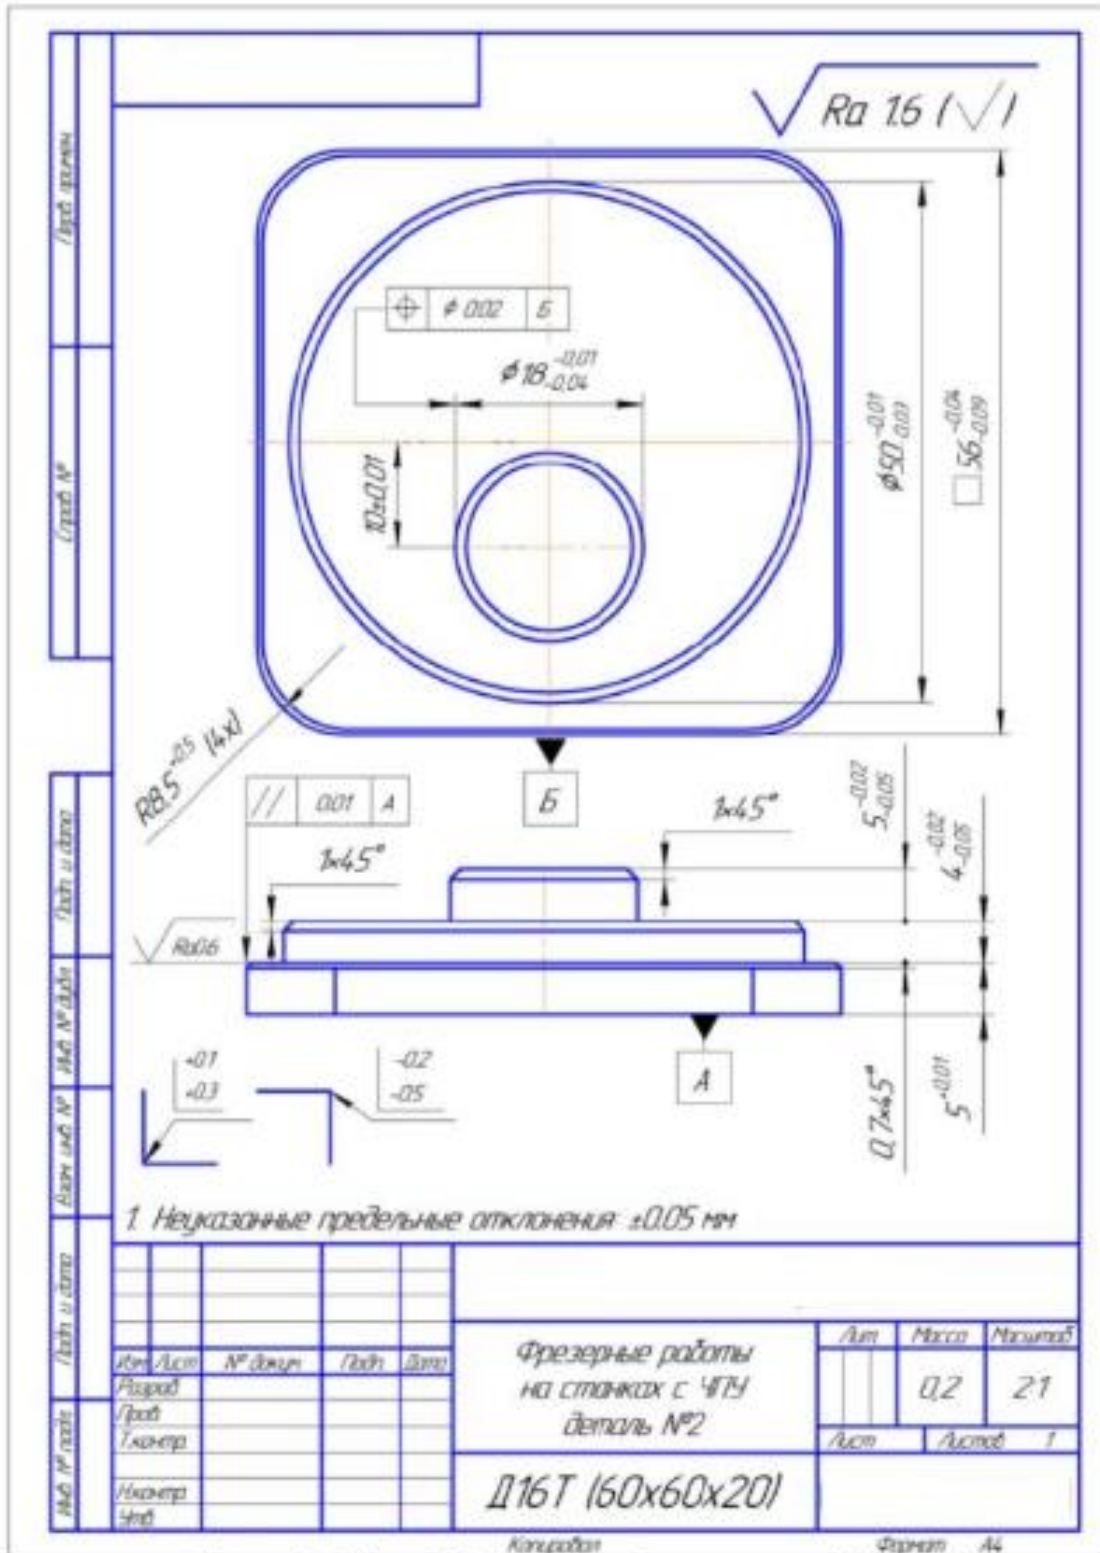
Деталь 2 Фрезерные работы на станках с ЧПУ
